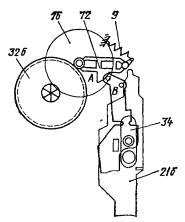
Механизм временного останова магинтной ленты: 9— пружина муфты сцепления; 216— толкательнай пружниа мгновенного «Стопа»; 326— подающий шпиндель; 34— пластина роликодержателя; 72— рычаг муфты сцепления; 76— диск муфты сцепления
